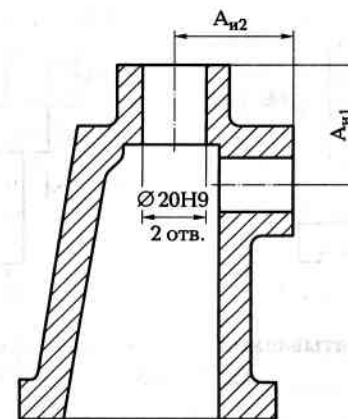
Эскиз обрабатываемой детали к заданию 1.30
